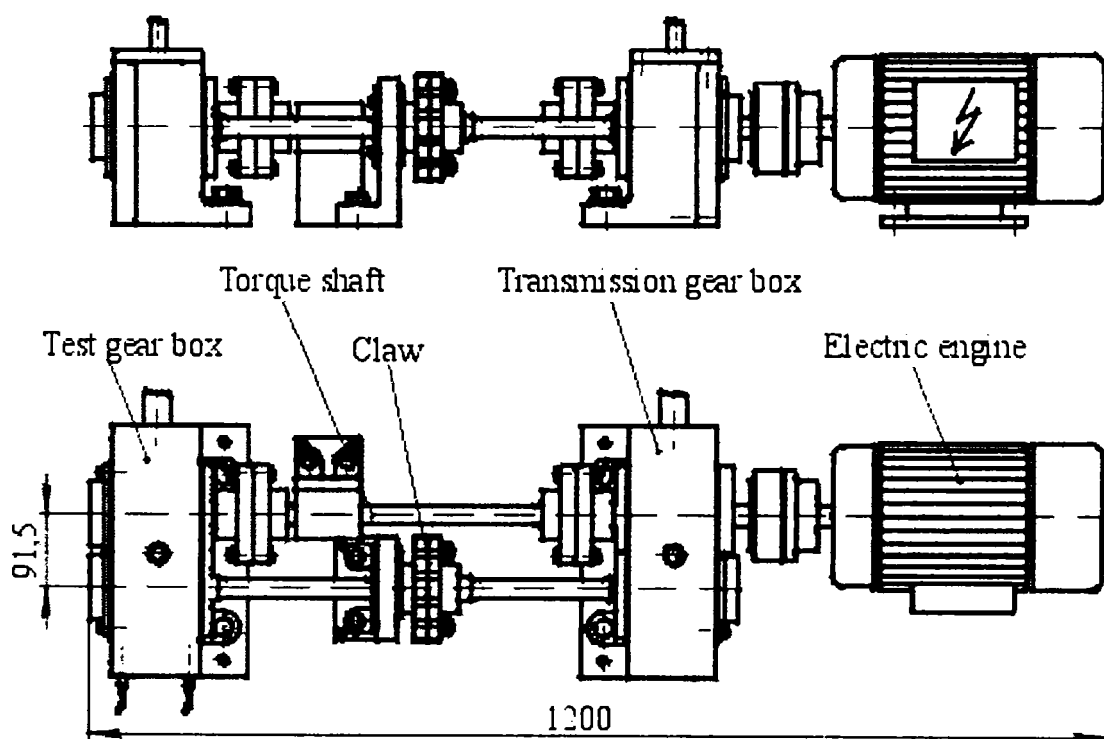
Schema clasică a standului de încercare în circuit închis, care conține motorul electric de acționare (Electric engine), o transmisie de returnare (Transmission gear box), un cuplaj pe tronsonul lent (Claw), arborele cu cuplajul tosiometric (Torque shaft) și transmisia de testat (Test gear box) [W20]
